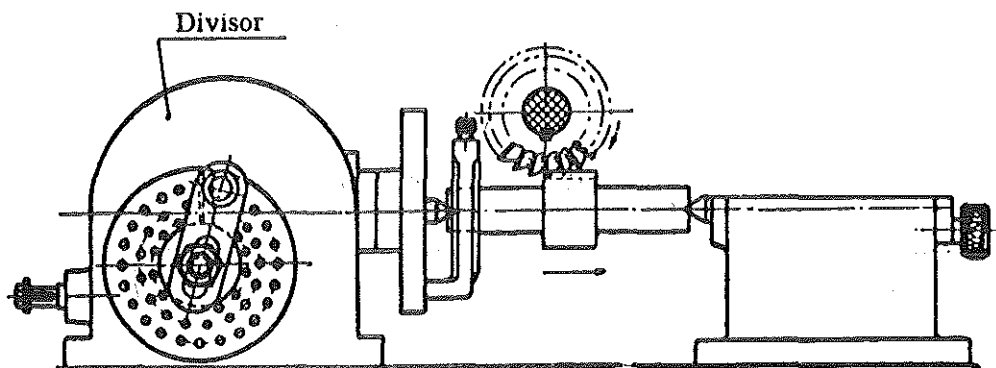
Montagem do divisor para fresar engrenagem reta.
